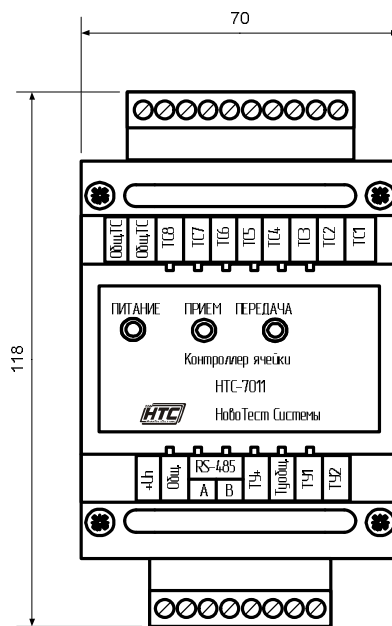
Внешний вид контроллера ячейки HTC-7011.
